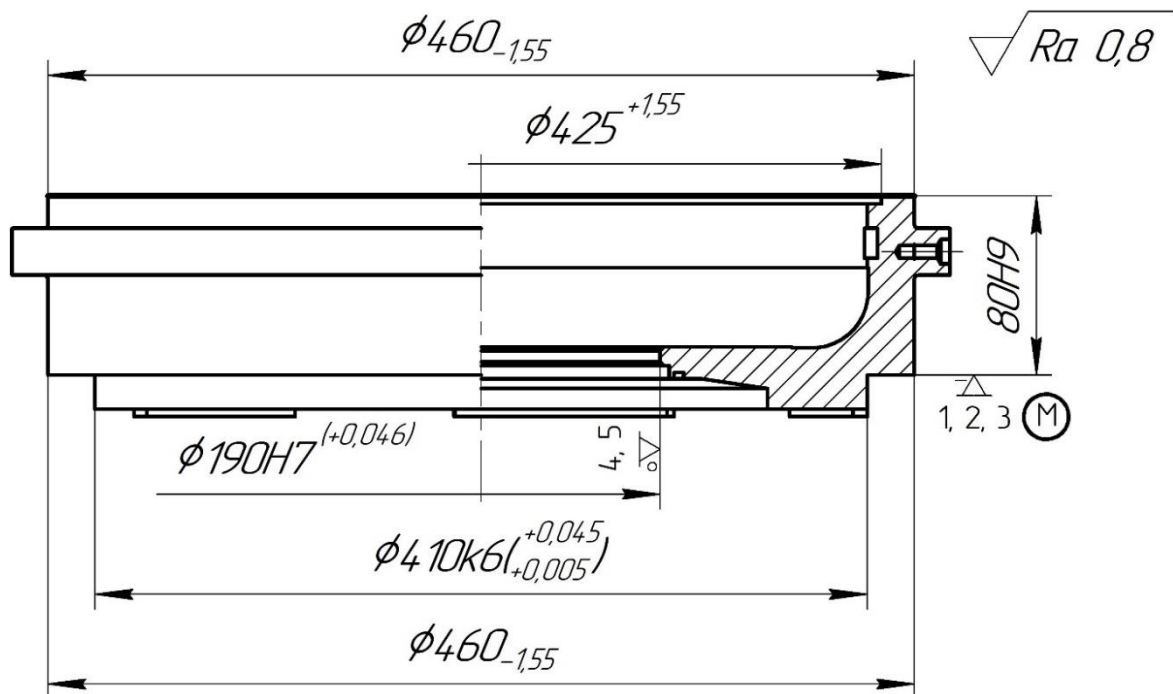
Ескіз заготовки на операції 045. Установ А
